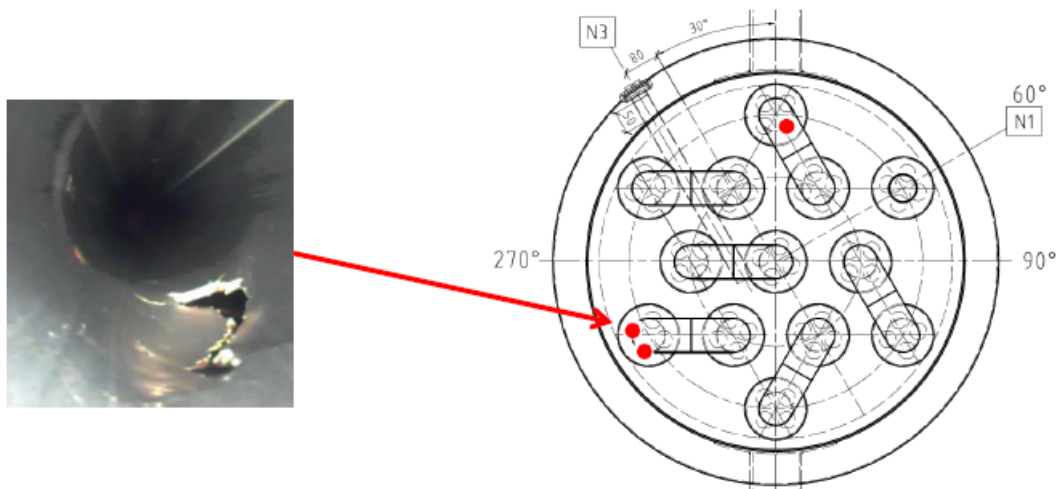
Trinca longitudinal situada a 1.200 mm do topo, encontrada na parede interna do tubo em ensaio endoscópico.
